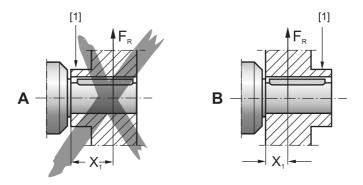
Disposição de montagem correcta de uma polia ou roda dentada
